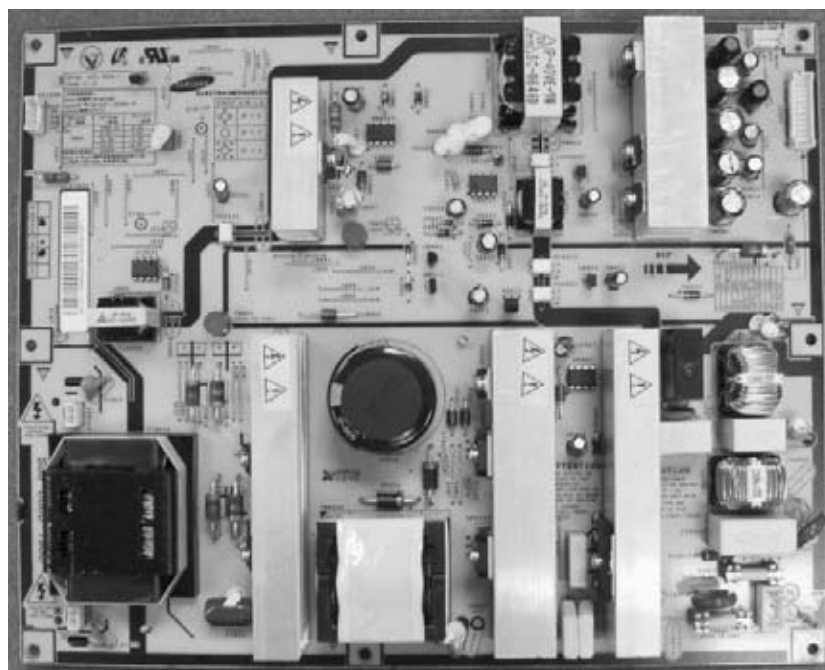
Внешний вид платы блока питания IP-231 135A
